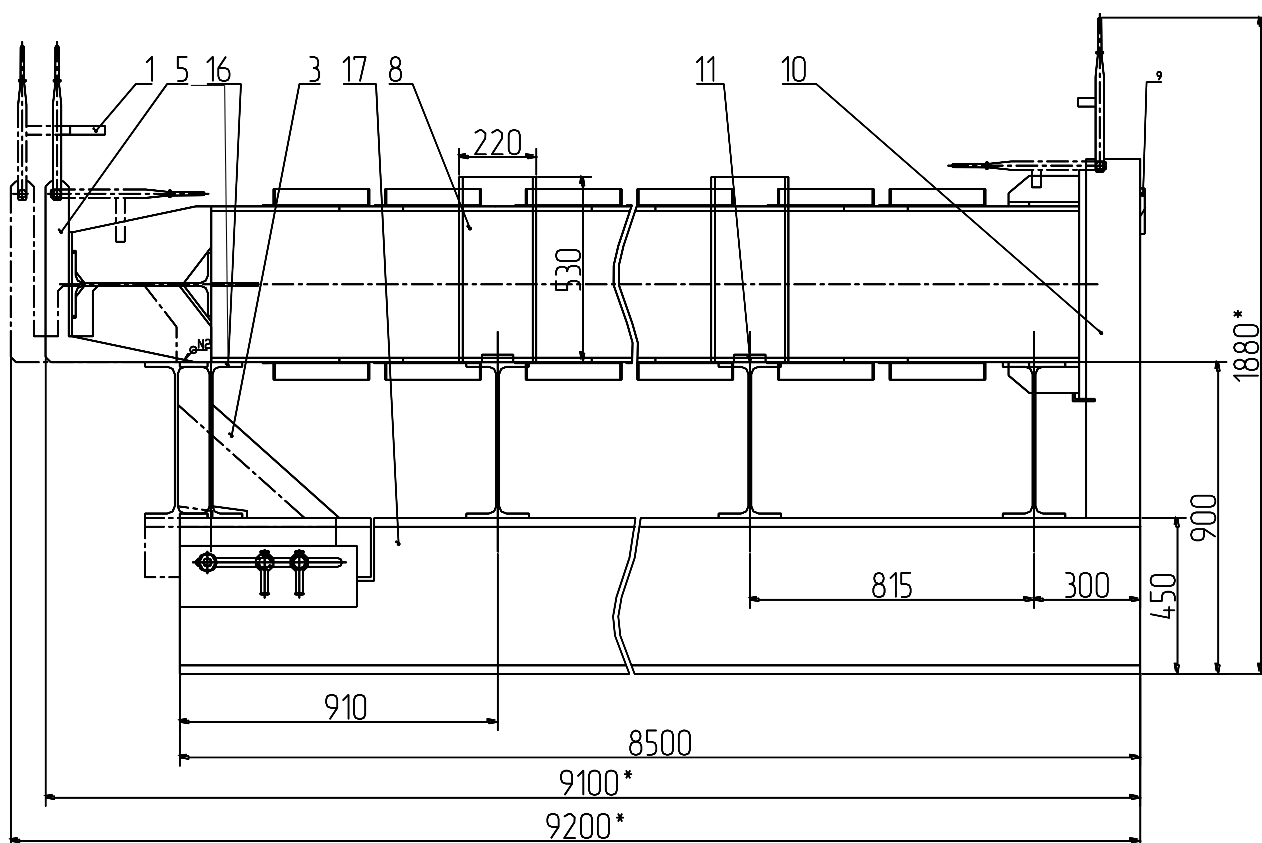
Общий вид приспособления для сварки стойки биллборда
